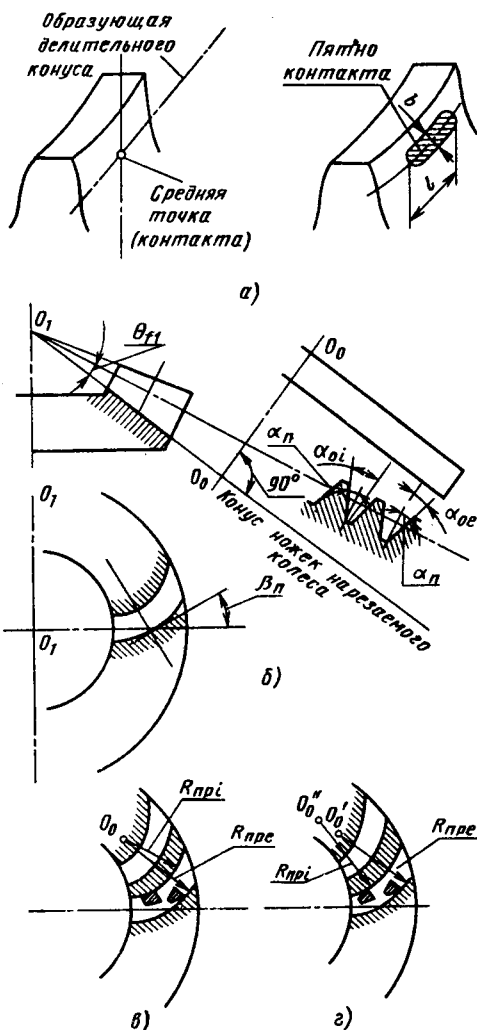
Определение правильного образования зубьев колес зуборезной головкой
